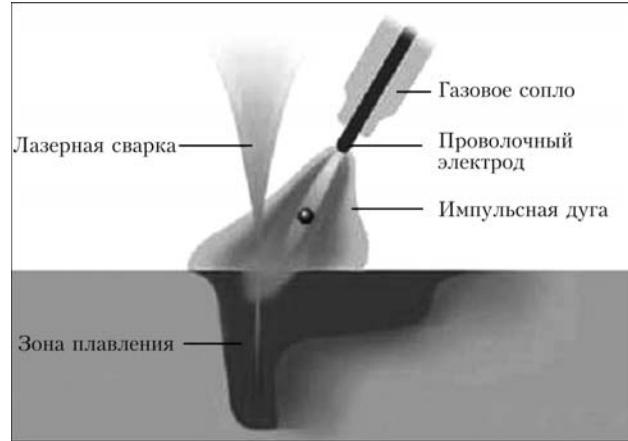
Схема гибридной лазерно-дуговой сварки
